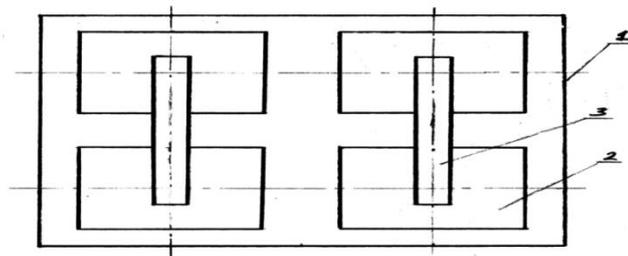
Магнитно – пневматическая подвеска (вид сверху)
